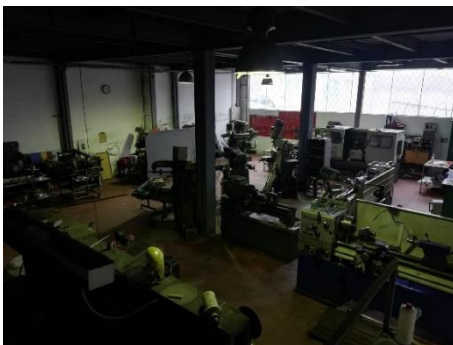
Avistamiento de la disposición en planta, de la empresa.
